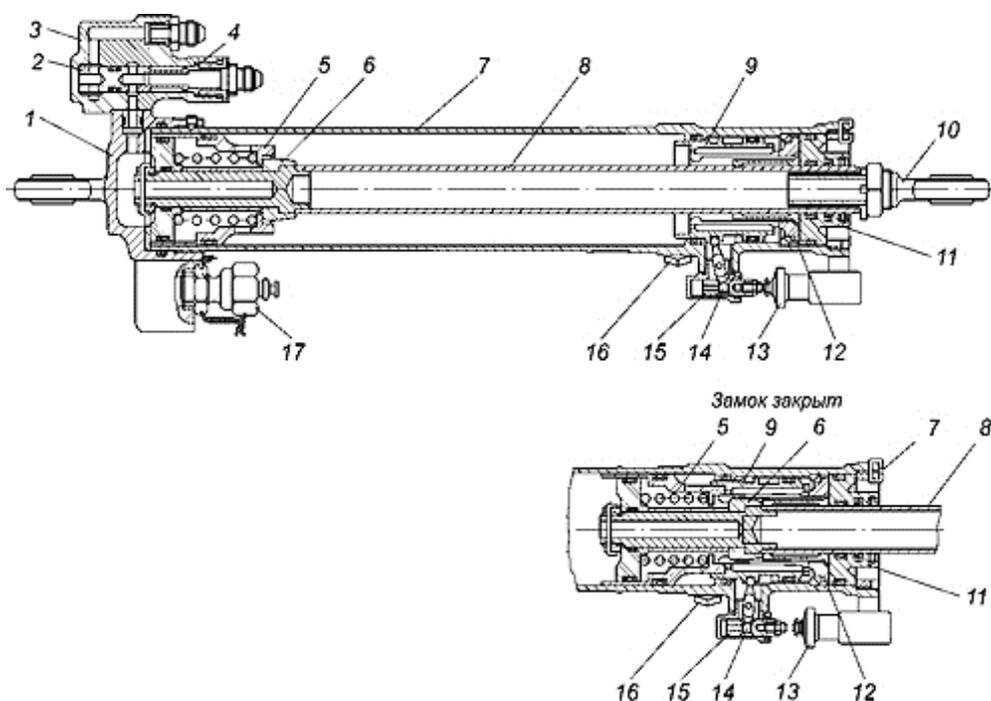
Цилиндр уборки-выпуска основных опор шасси¹²:
